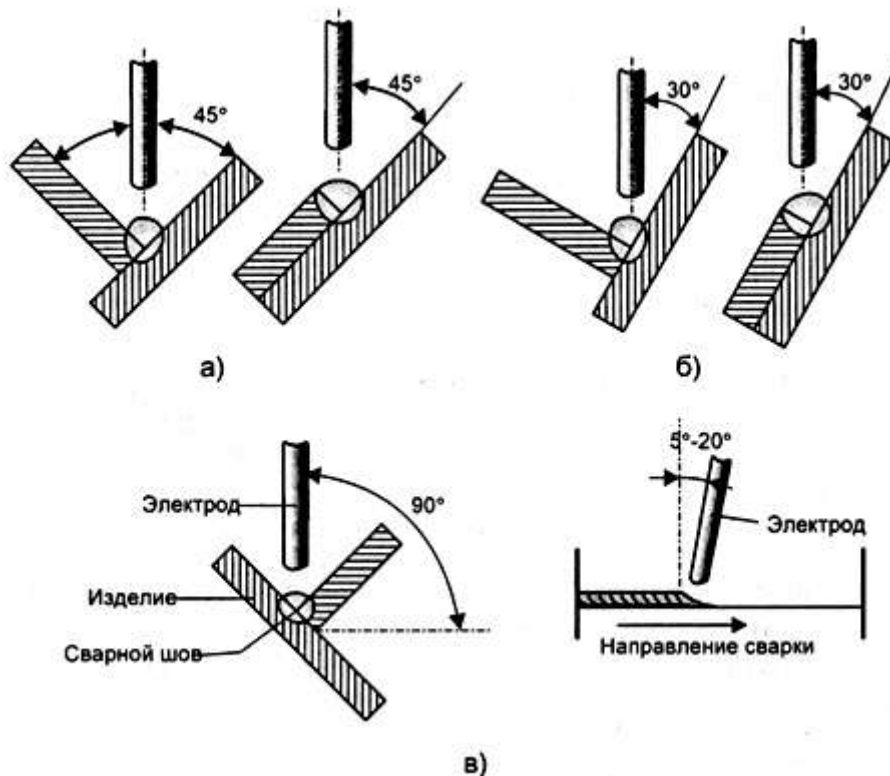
Положение электрода при сварке «в лодочку»: а) сварка в симметричную «лодочку»; б) сварка в несимметричную «лодочку»; в) пространственное положение электрода.
